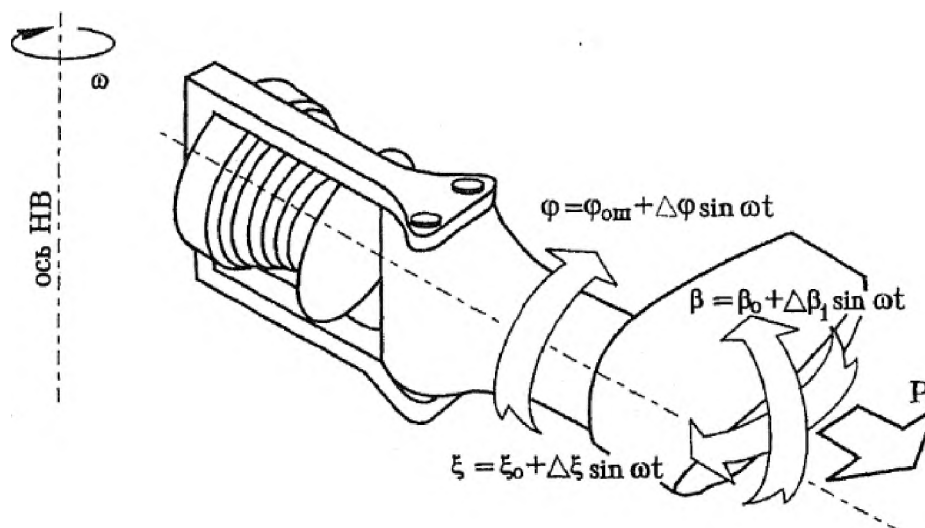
Схема нагружения сферического эластомерного подшипника.
